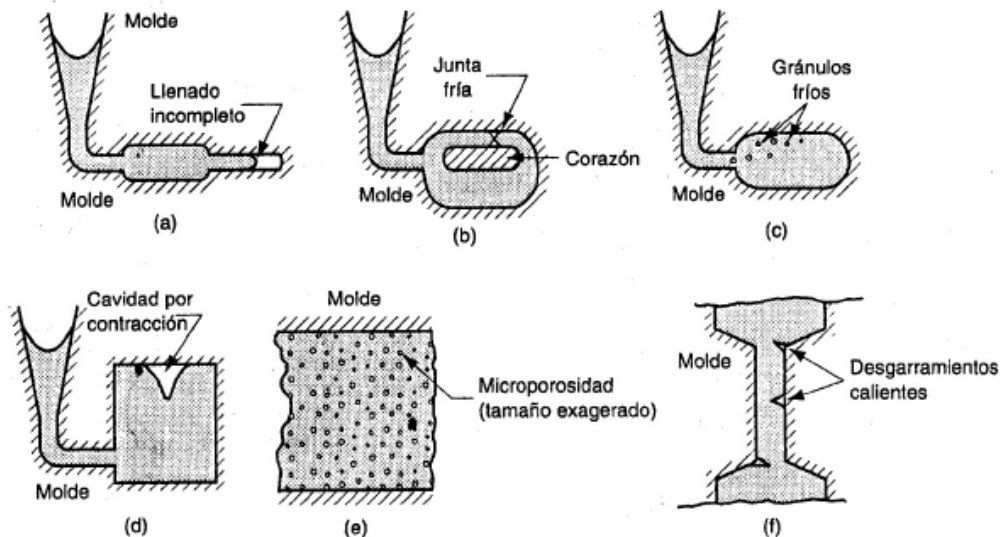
Algunos defectos en los productos de fundición.
